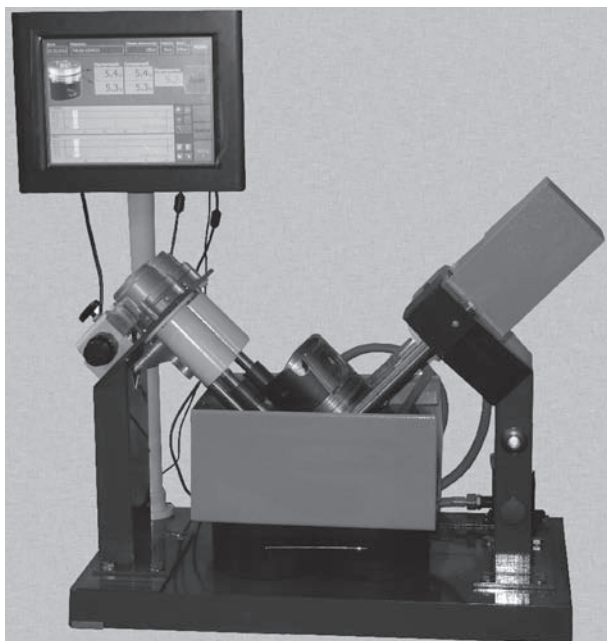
Установка для неразрушающего контроля качества сцепления нирезистивных вставок в поршнях дизельных двигателе
